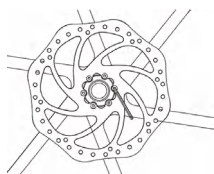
Anziehen der Bremsscheibenbefestigungsschrauben mit einem 3mm-Innensechskantschlüssel
